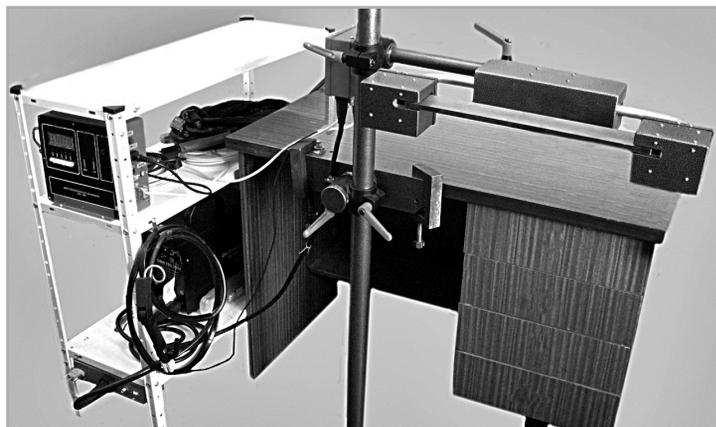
Общий вид тренажера сварщика ТСДС-06М
